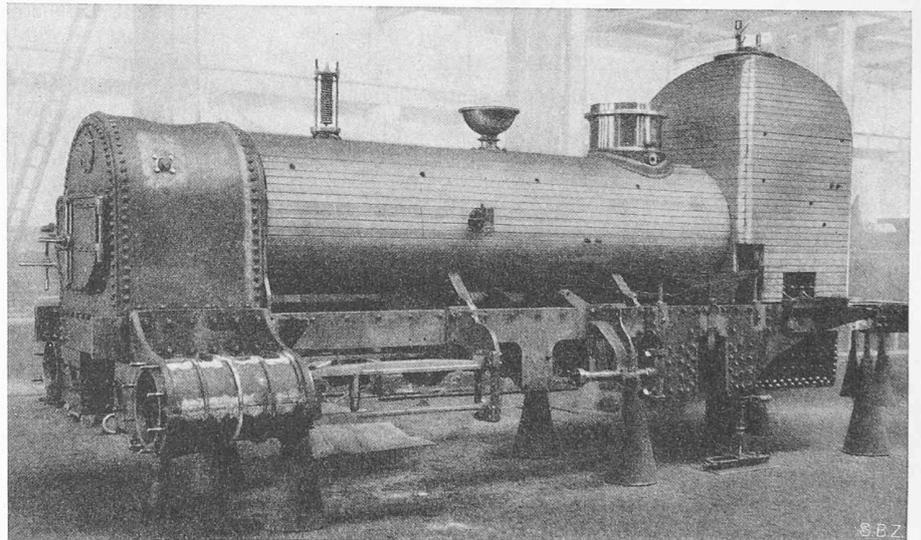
Rahmen mit Zylinder und aufgebautem Kessel
